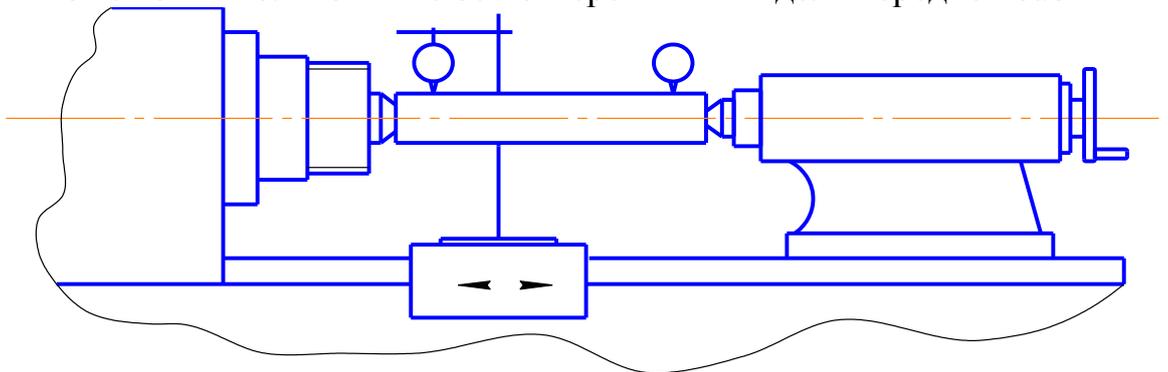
Схема установки индикатора для проверки расположения осей отверстия шпинделя передней бабки и пиноли на одинаковой высоте над направляющими станины и суппорта
